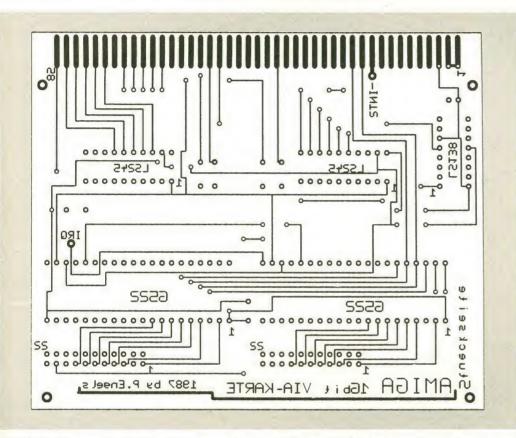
Das Layout für die Bestückungsseite der VIA-Karte im Maßstab 1:1 (spiegelverkehrt)
